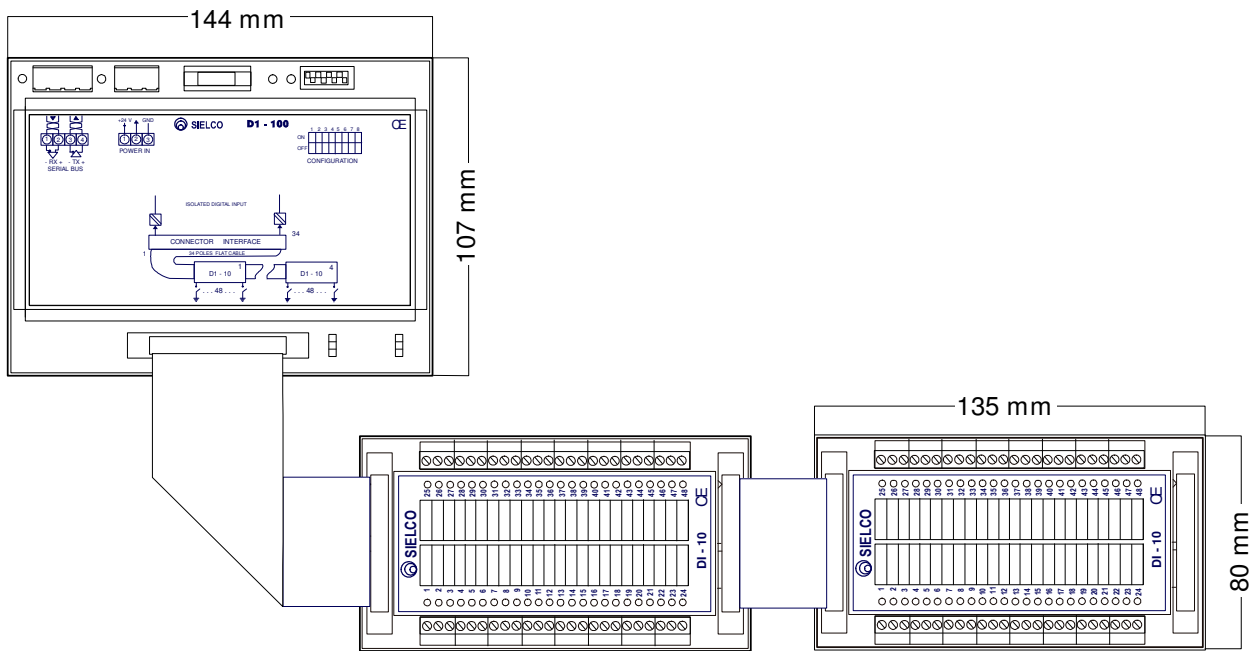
Dimensioni dei moduli D1-100 e D1-10
